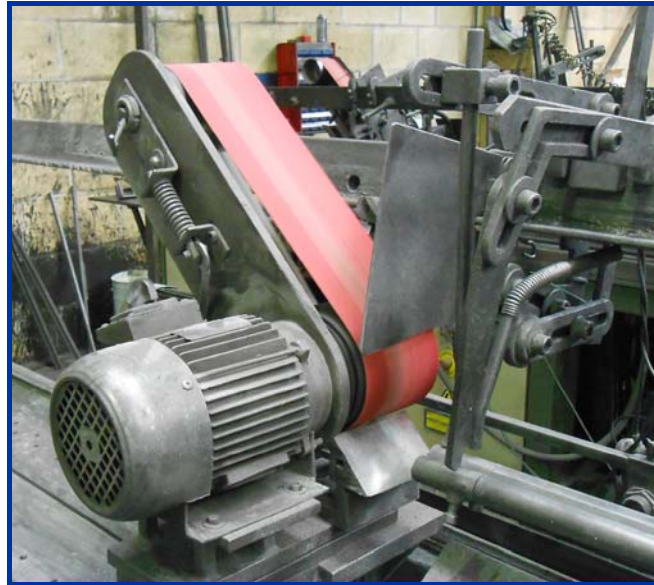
Máquina preformadora para puntas lijadas. Detalle de la lijadora.
